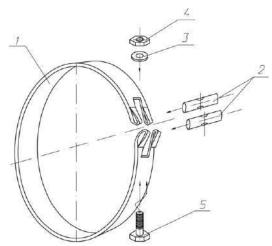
Общий вид КМЧ для установки ППТП с корпусом типа «К1» на трубопроводе (1- лента, 2- стержни с отверстиями, 3- шайба, 4- гайка, 5- болт)
